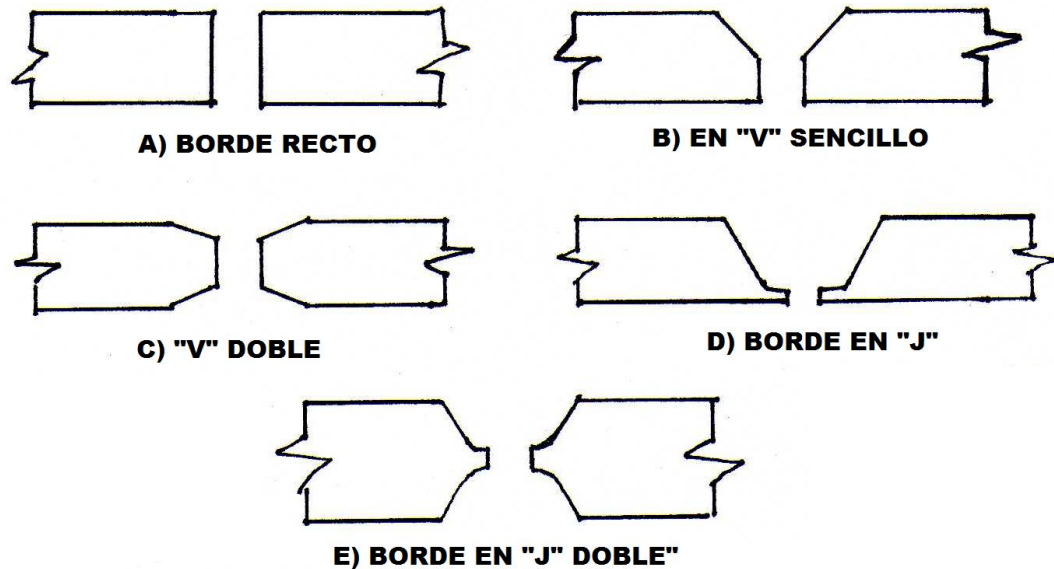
Soldaduras aplicables en junta a tope
